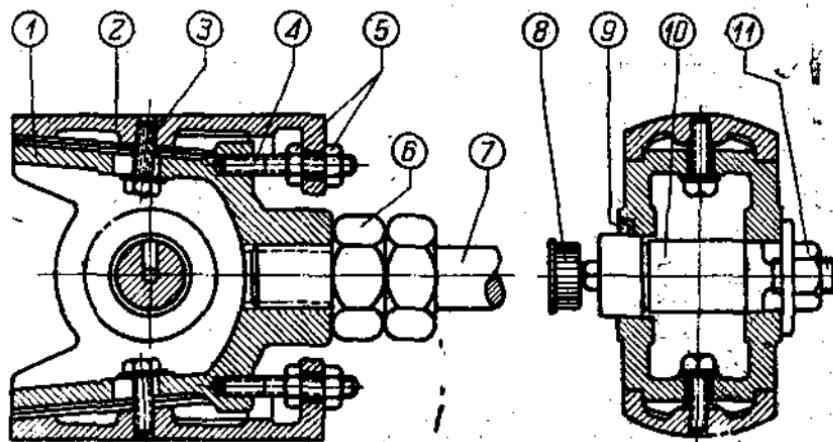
Крейцкопф воздушного компрессора типа Бородино.
